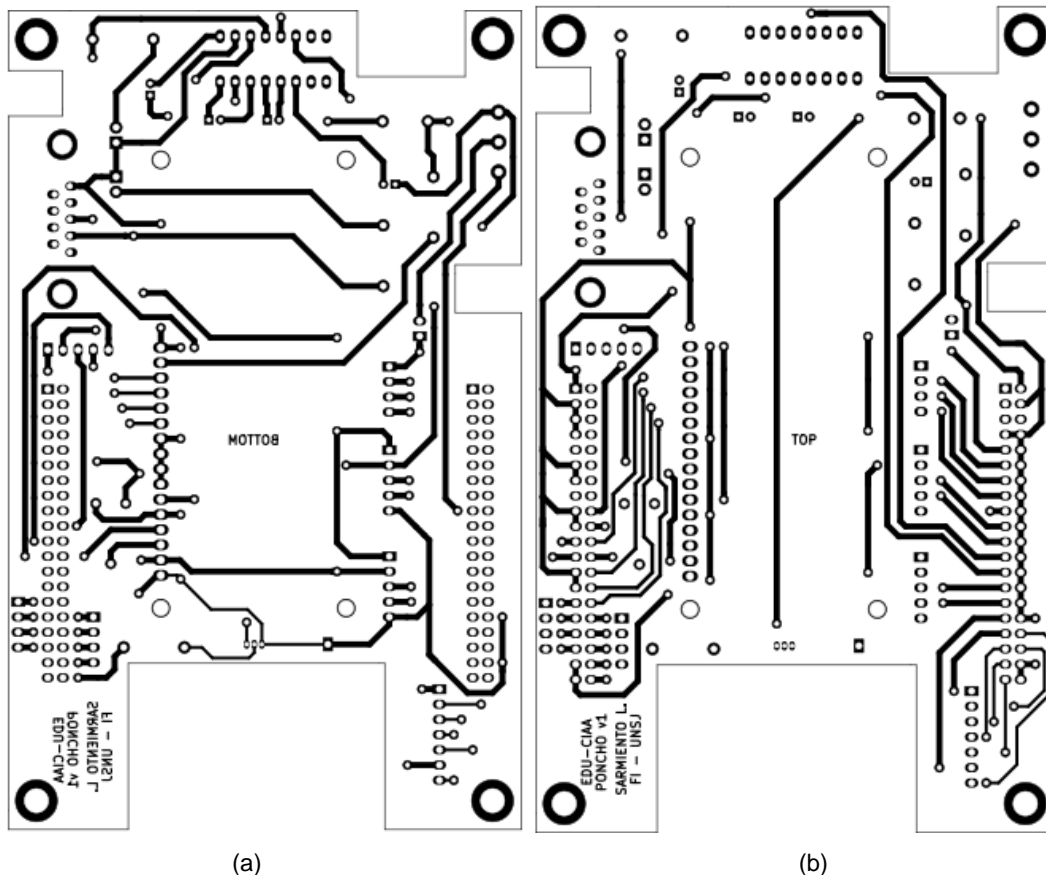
, Diseño final de placa circuito impreso parte de inferior (a) y la parte superior (b)
